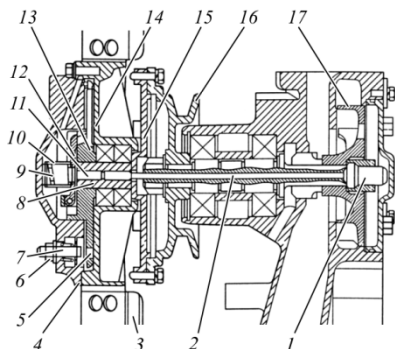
Привод вентилятора с вязкостной муфтой: 1 – термозлемент; 2 – шток; 3 – лопасть вентилятора; 4 – крышка ведомая; 5 – отверстие для стопорения; 6 – гайка стопора; 7 – стопор; 8 – хвостовик приводного вала; 9 – пружина возвратная; 10 – обойма; 11 – толкатель; 12 – клапан муфты; 13 – диск ведущий; 14 – диск ведомый; 15 – диск привода; 16 – шкив привода жидкостного насоса; 17 – крыльчатка жидкостного насоса
